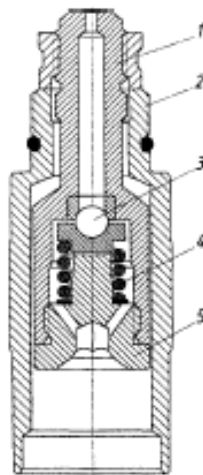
Зворотний клапан системи зливу палива: 1 - корпус клапана; 2 - зовнішній корпус; 3 - кульковий клапан; 4 - притискна пружина; 5 - нарізна пробка
